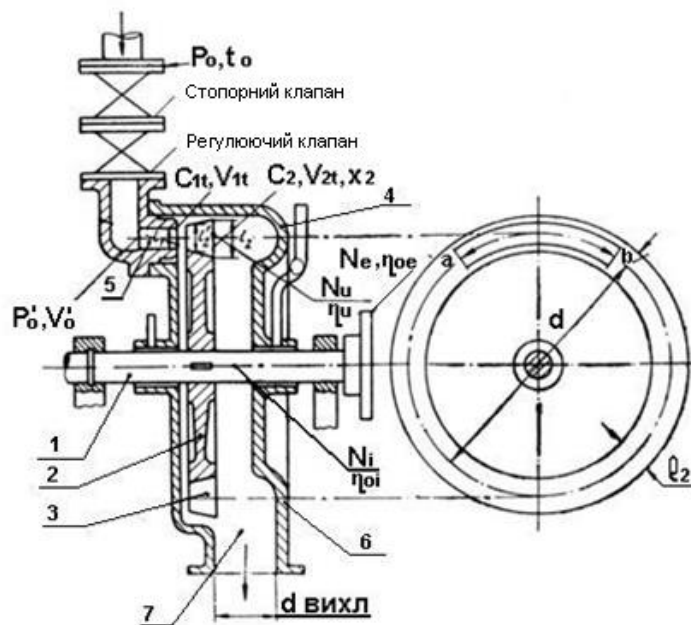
Схема одноступеневої парової турбіни: 1 – вал турбіни; 2 – диск; 3 – робочі лопатки; 4 – верхня половина корпусу турбіни; 5 – сопло; 6 – нижня половина корпусу; 7 – вихідний патрубок.
